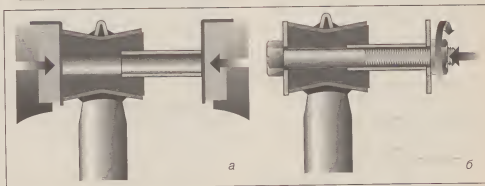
Запрессовка стальной втулки: а – в тисках; б – с помощью болта.
